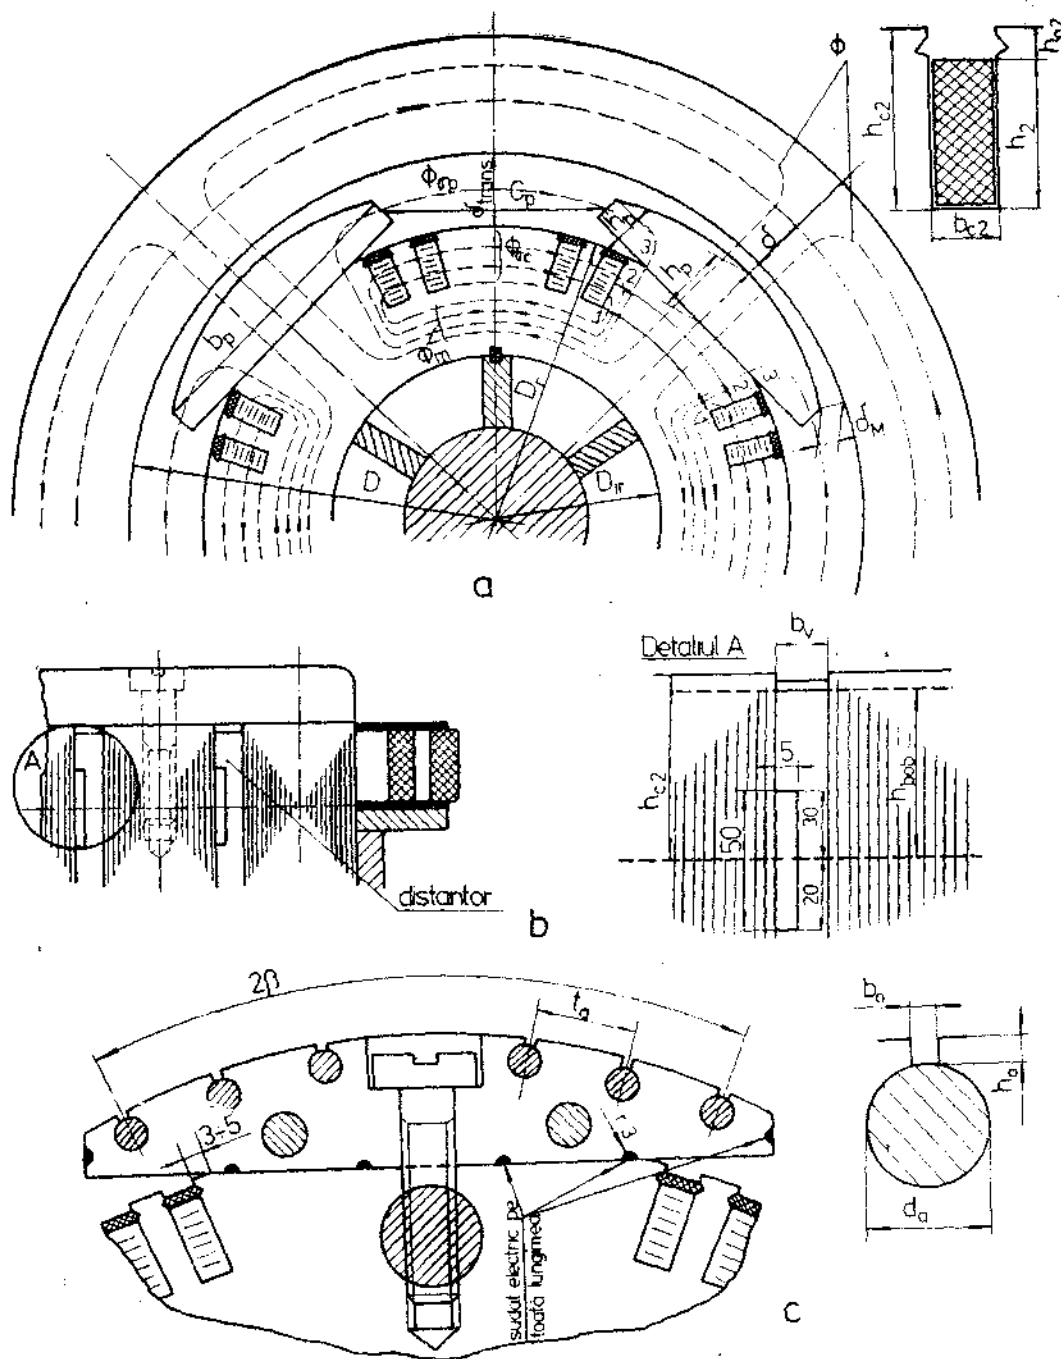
Mașina sincronă cu rotorul în variantă combinată:
